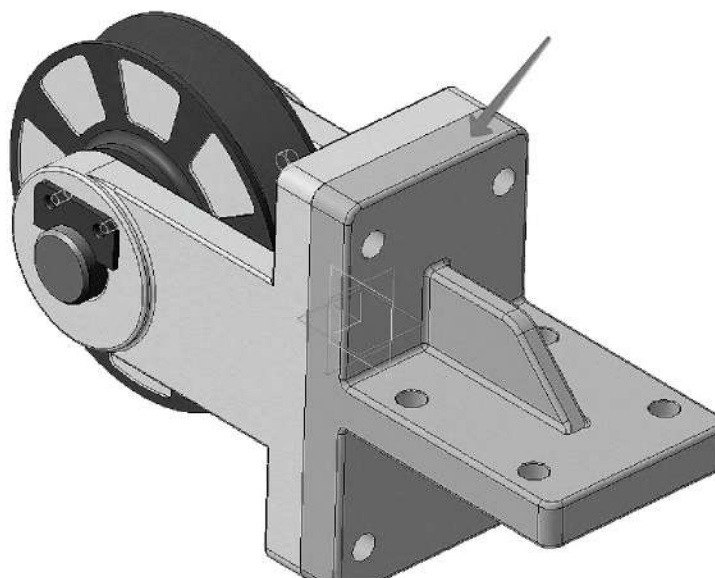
Деталь «Кронштейн» сборочной модели «Блок направляющий»
